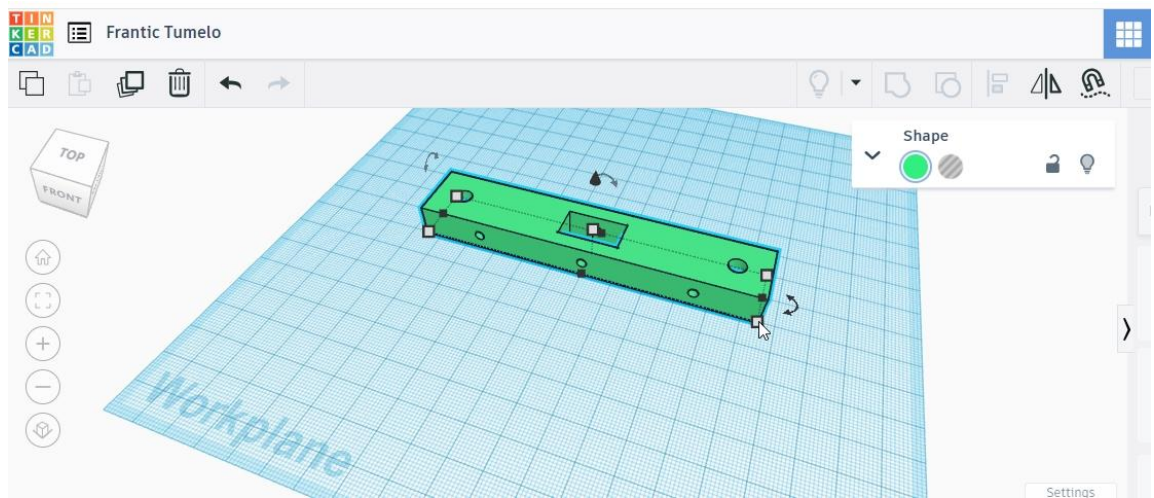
Зовнішній вигляд деталі Y2_CNC.
